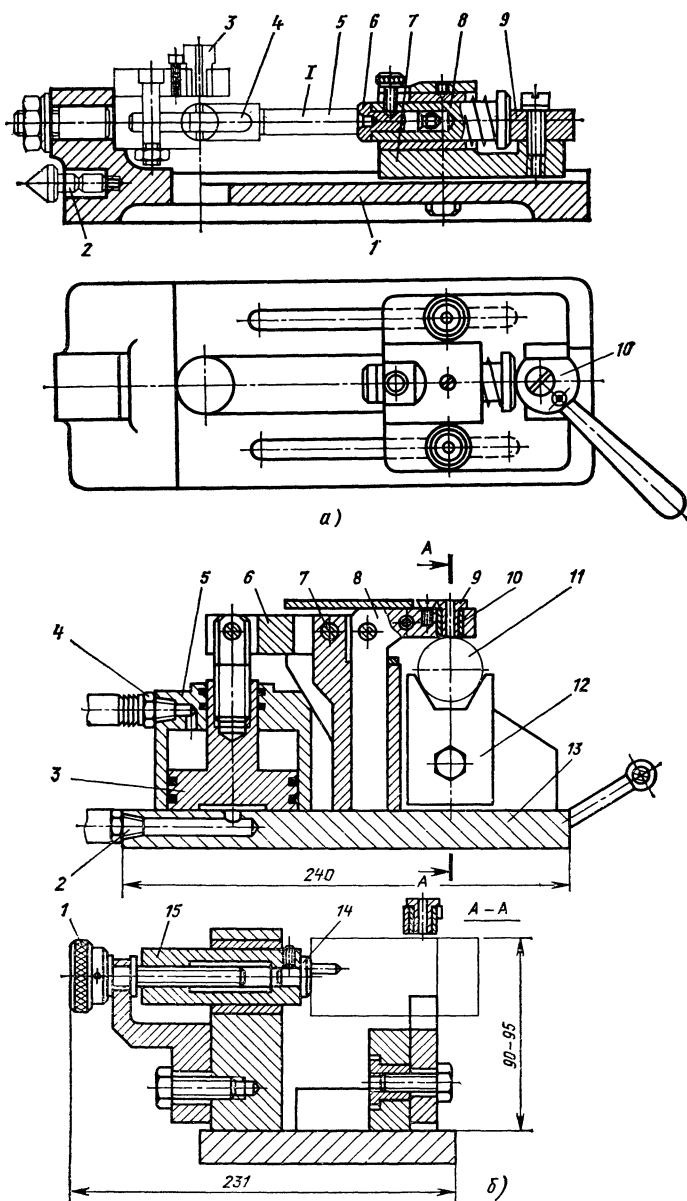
Переналаживаемые кондукторы для сверления радиально расположенных отверстий: а — на концах деталей типа валиков, тяг и вилок (I — обрабатываемая деталь); б — в валиках и шестигранниках
